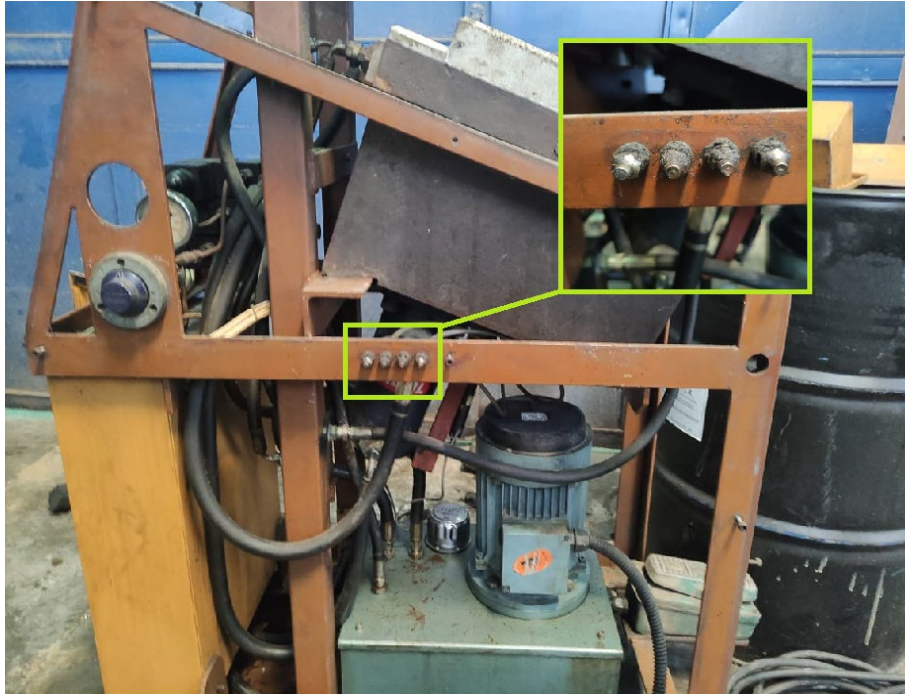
Orificios para lubricación de la máquina Soldadora en frío.
